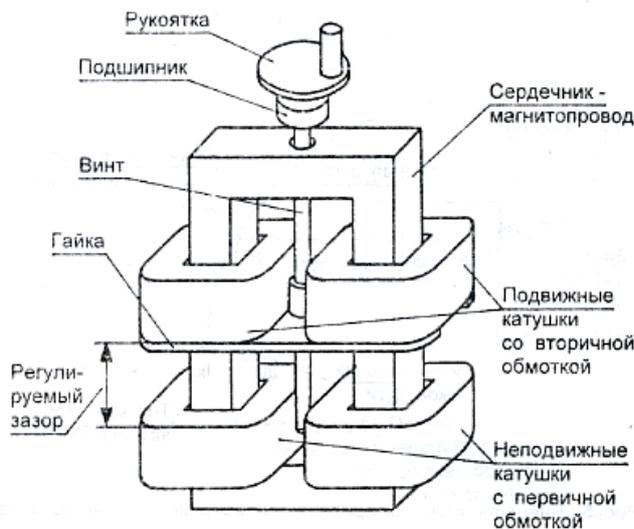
Конструктивная схема сварочного трансформатора с подвижными катушками вторичной обмотки
